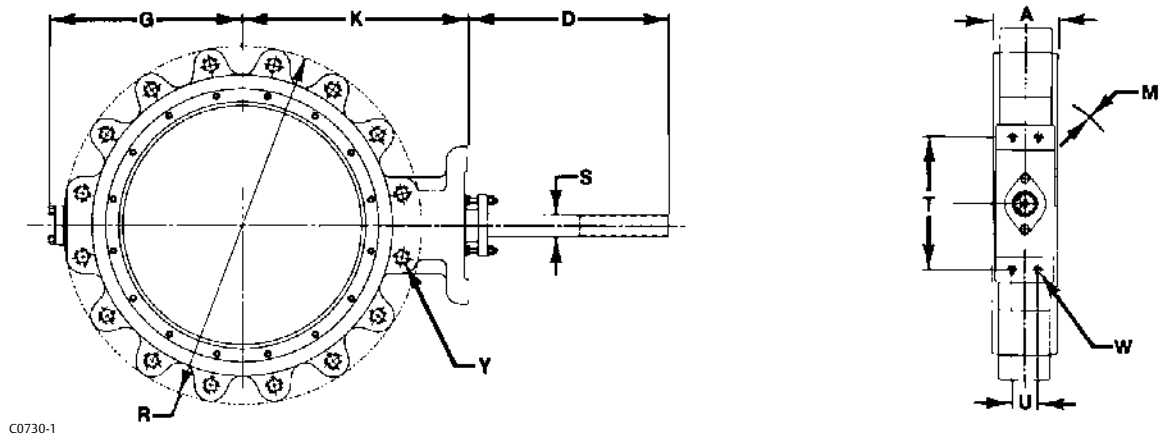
Размеры затвора 8532 в однофланцевом корпусе с проушинами
